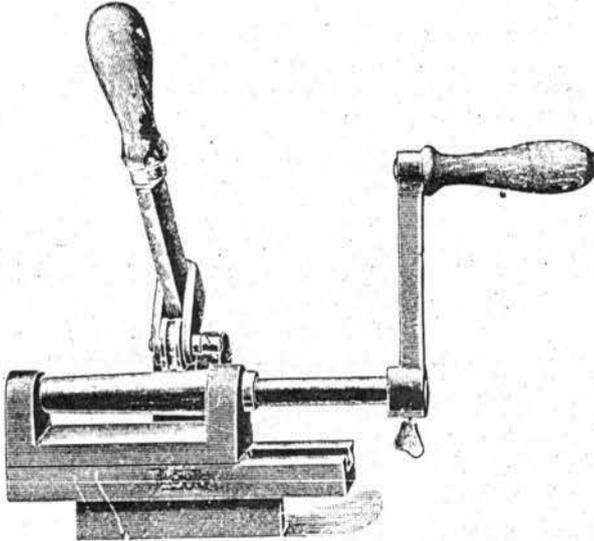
Die bisherige Maschine, Druckerzeugung mittels Handhebel.
